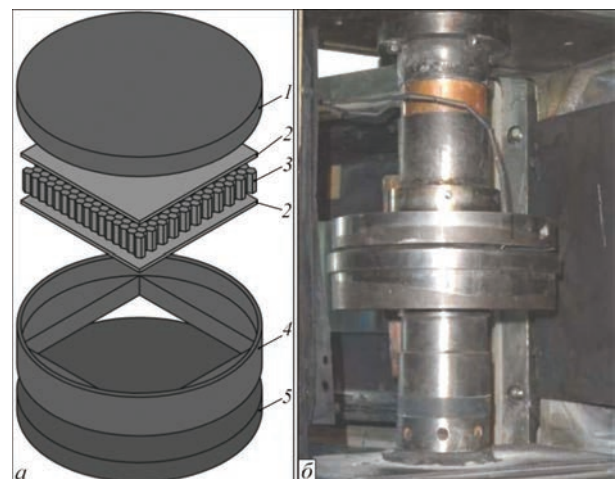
Схематическое изображение оснастки для сварки трехслойных сотовых панелей (а) и рабочая камера с установленной в ней оснасткой (б): 1 — верхний фланец; 2 — обшивка; 3 — сотовый заполнитель; 4 — ограничивающая втулка; 5 — нижний фланец
